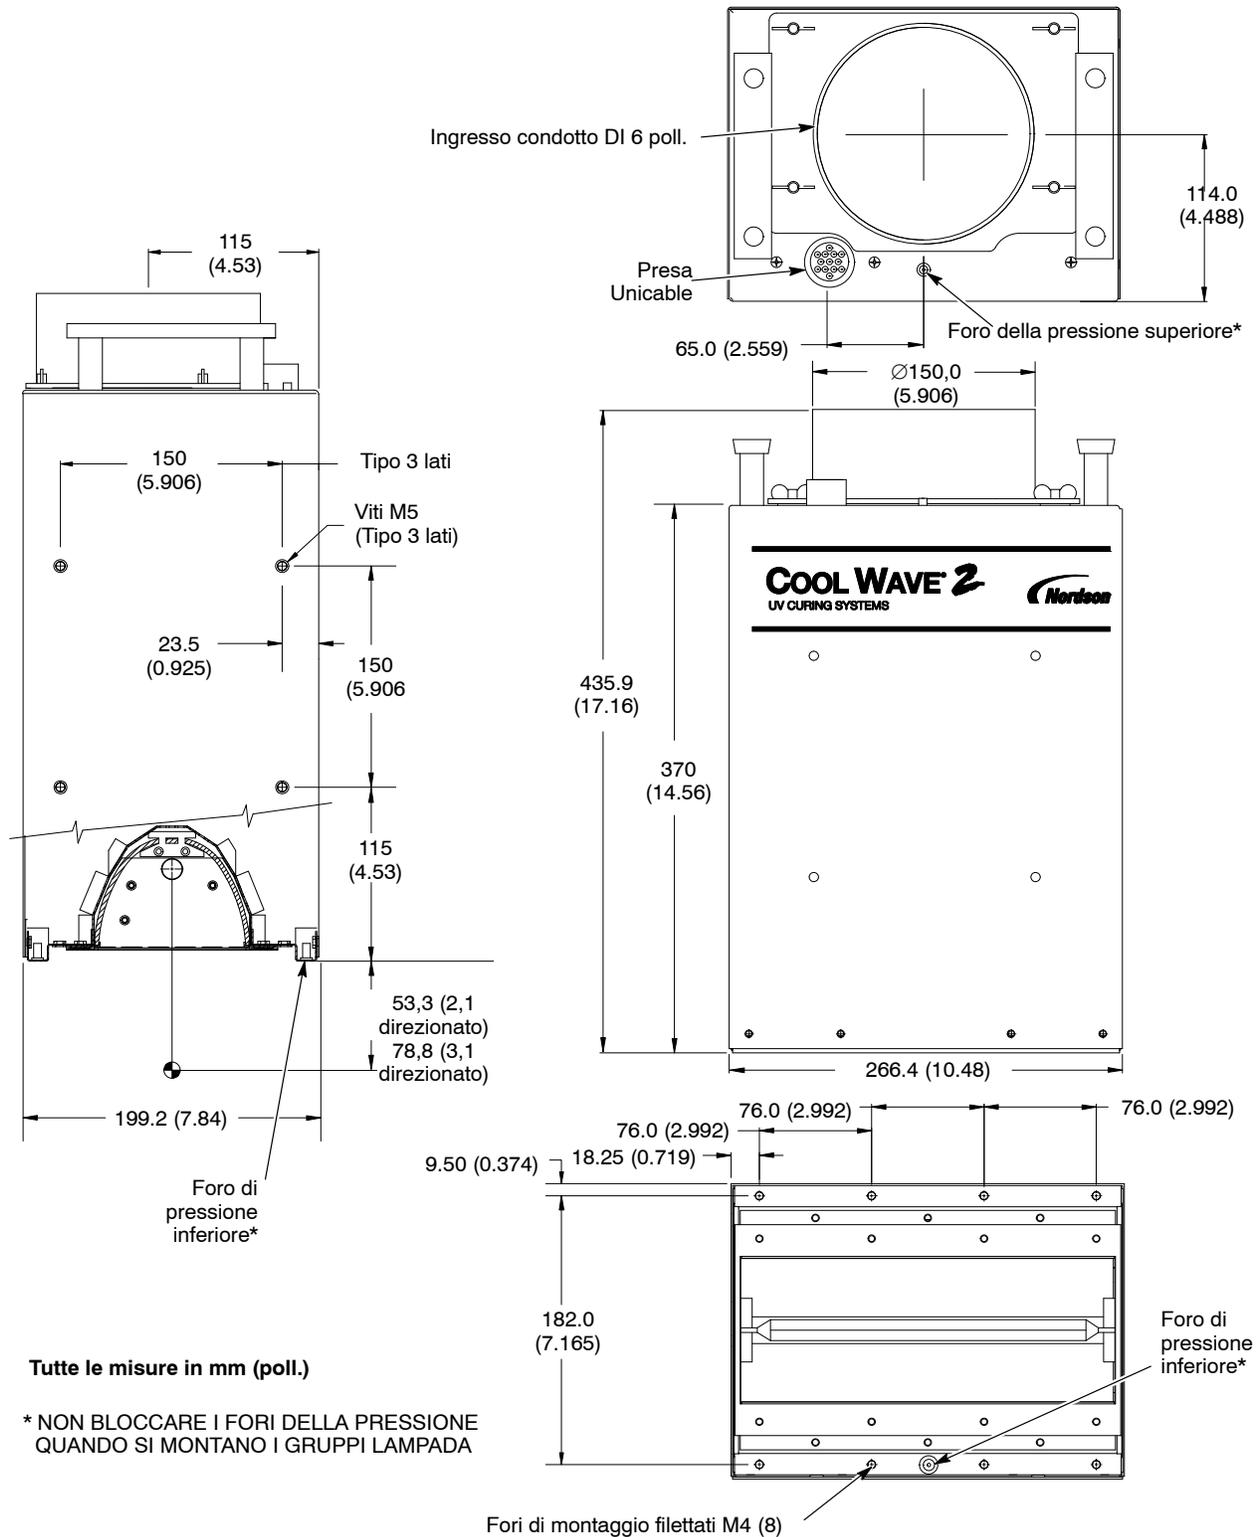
Dimensioni del gruppo lampada – versione con soffiante esterno
